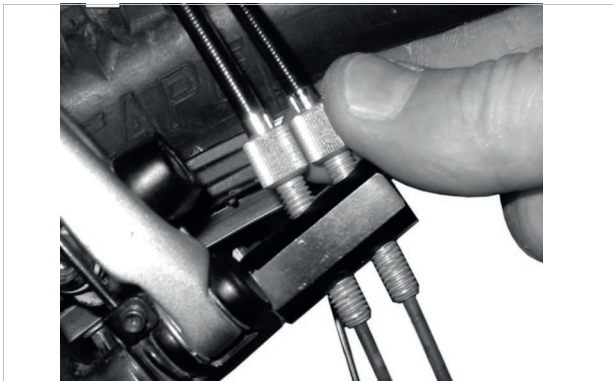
ROHLOFF-Naben Versionen mit interner Schaltansteuerung haben die Zugeinsteller am Zuggegenhalter
